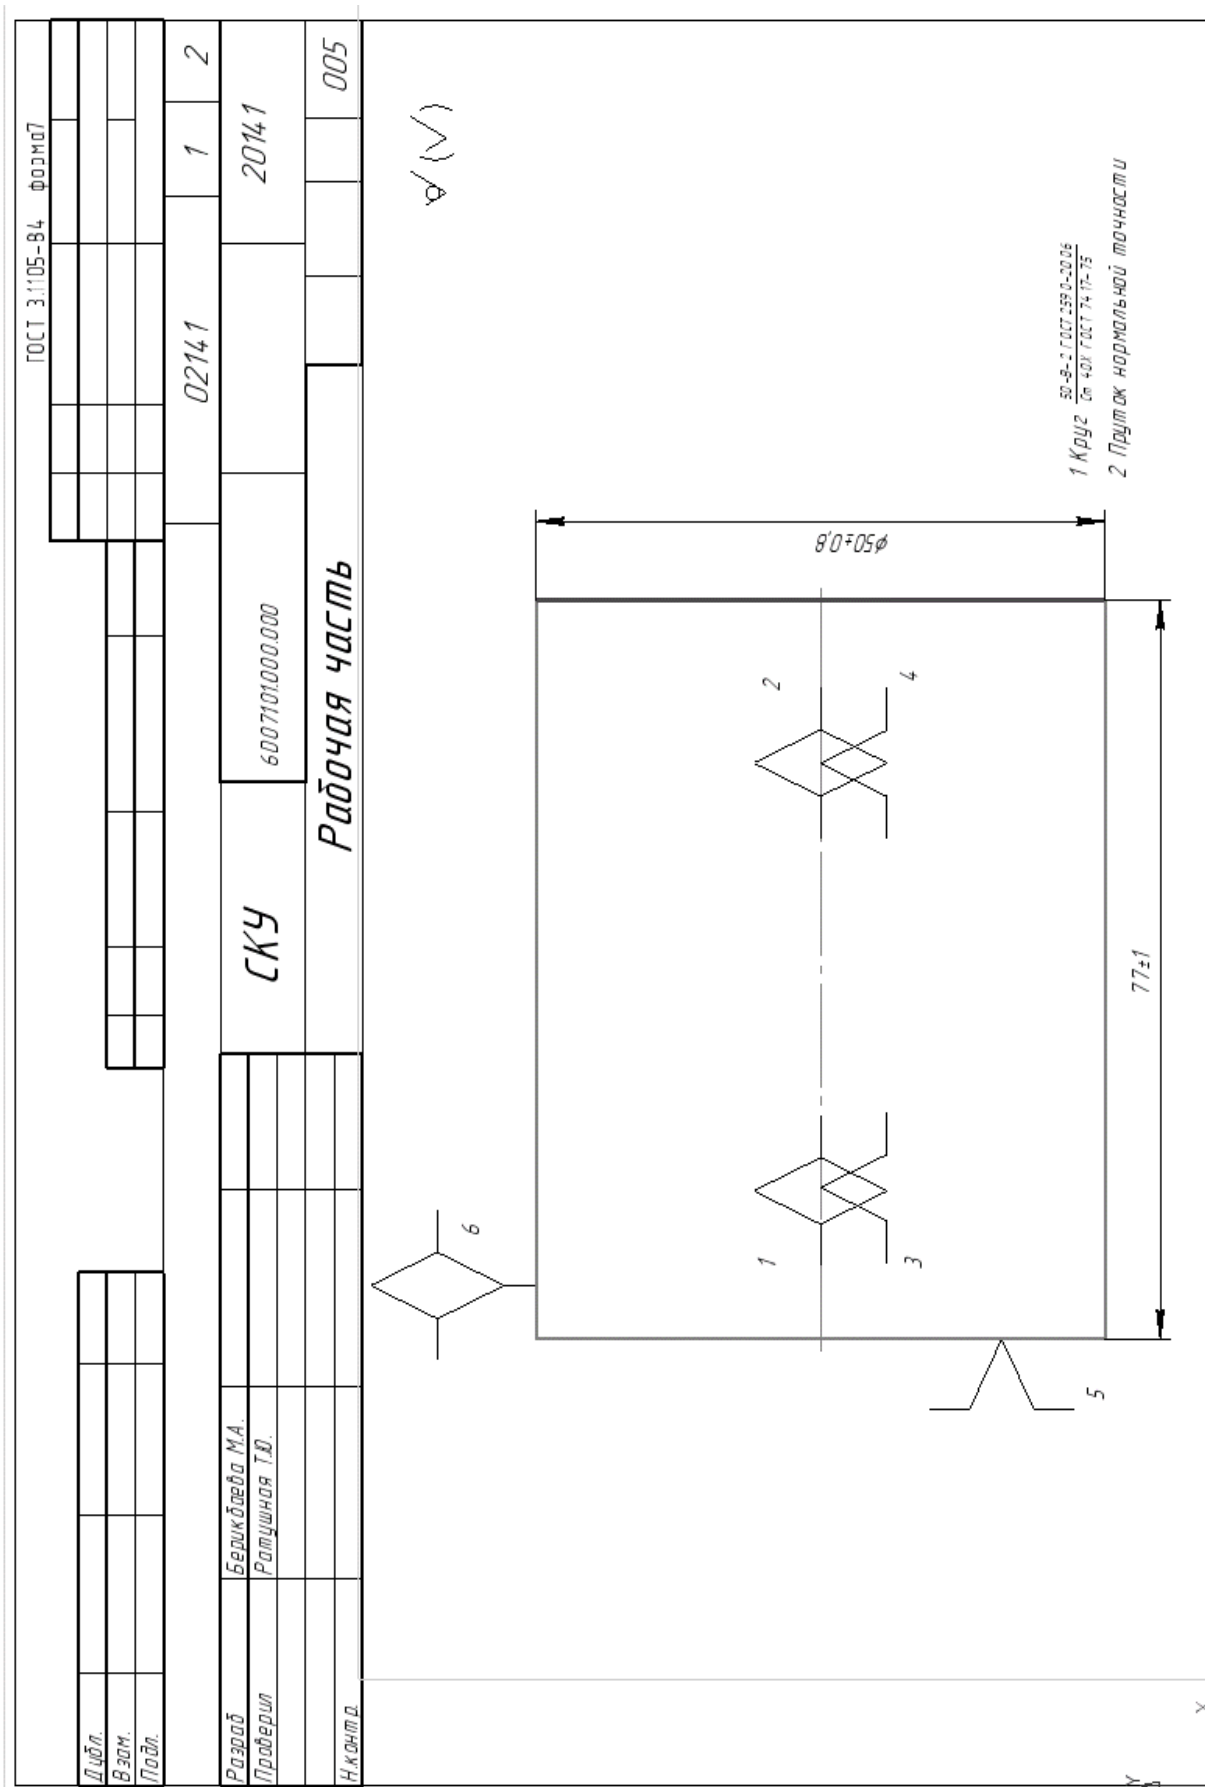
Карта эскизов изготовления комбинированного инструмента,
